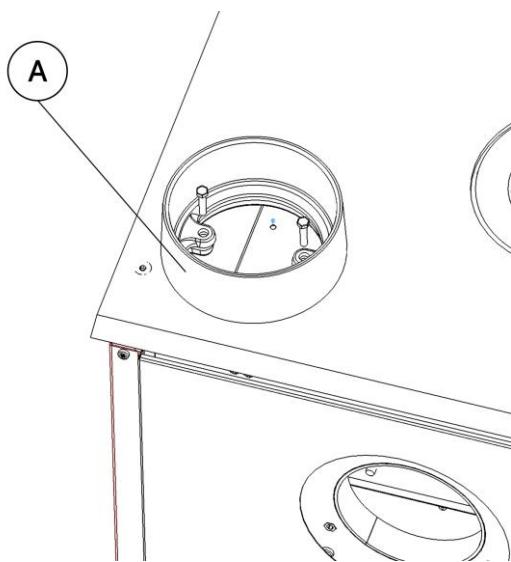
Colocamos a flange superior de saída de fumos.A
